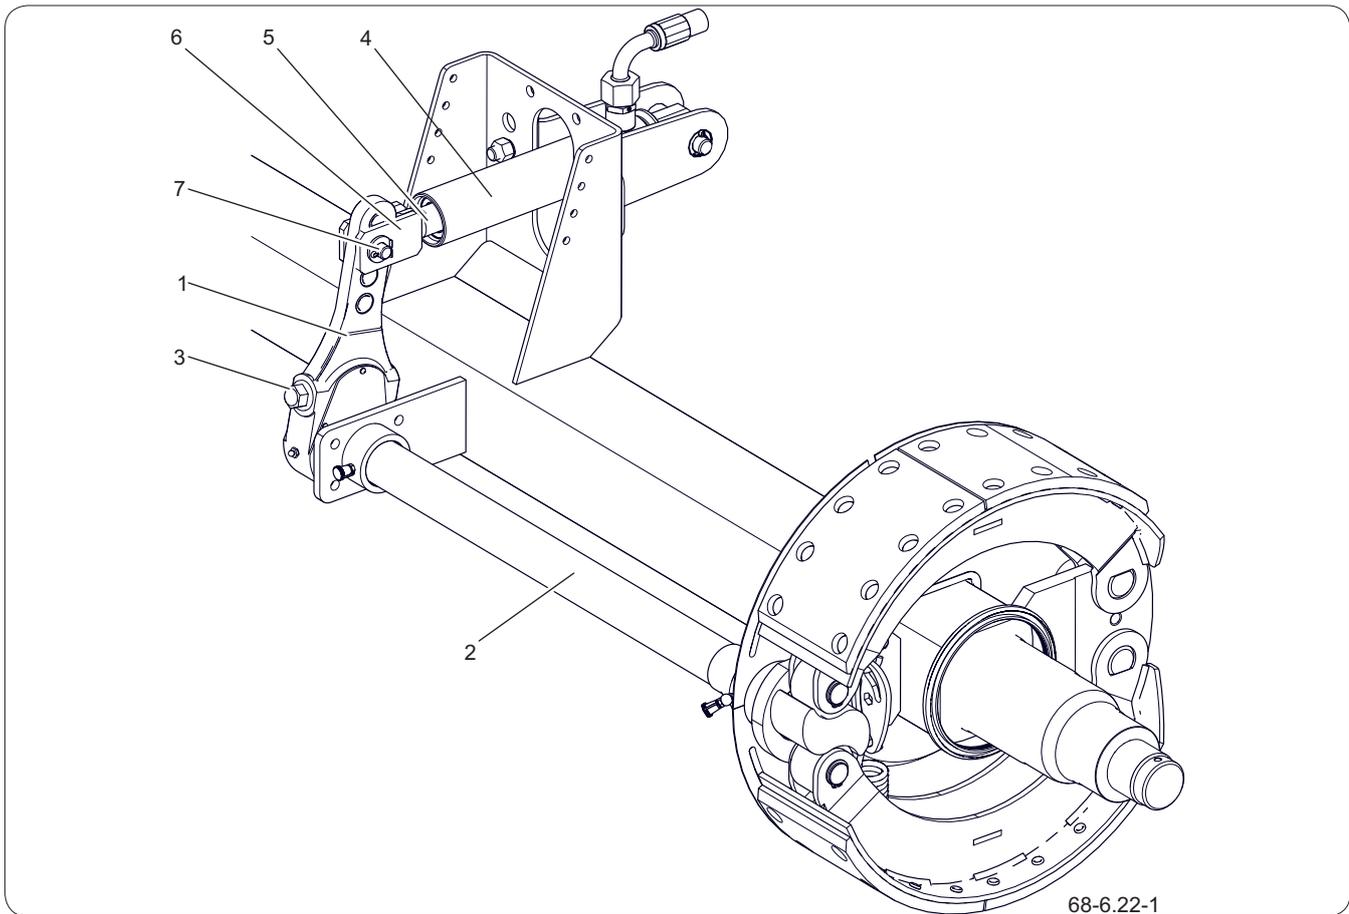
Construction du frein hydraulique de l'essieu moteur
